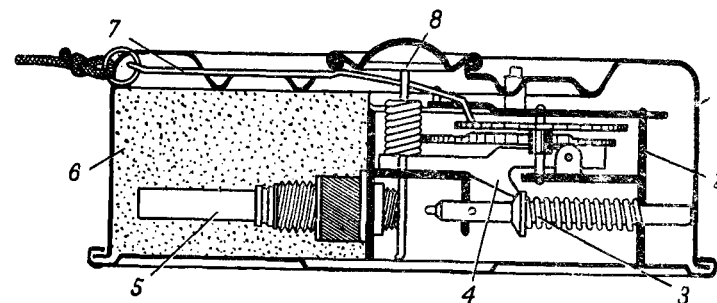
Немецкий разгрузочный взрыватель EZ. SM2:
